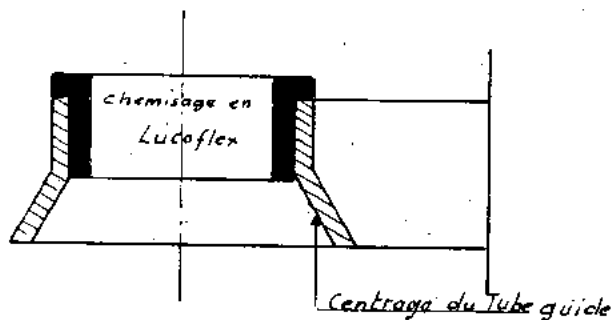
c. — Isolement entre tube guide et casing de forage.
